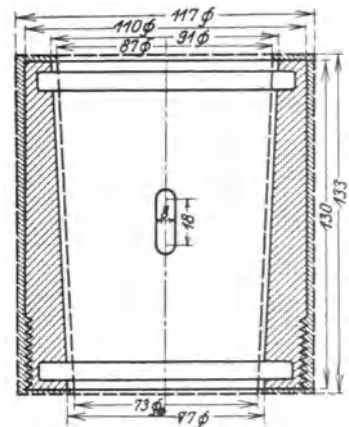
Abmessungen des Gußstückes und der bearbeiteten Versuchslagerbüchse.
